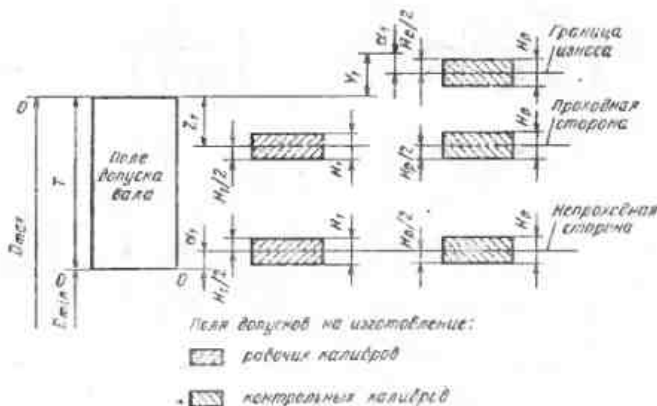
Схема расположения полей допусков калибров для валов
